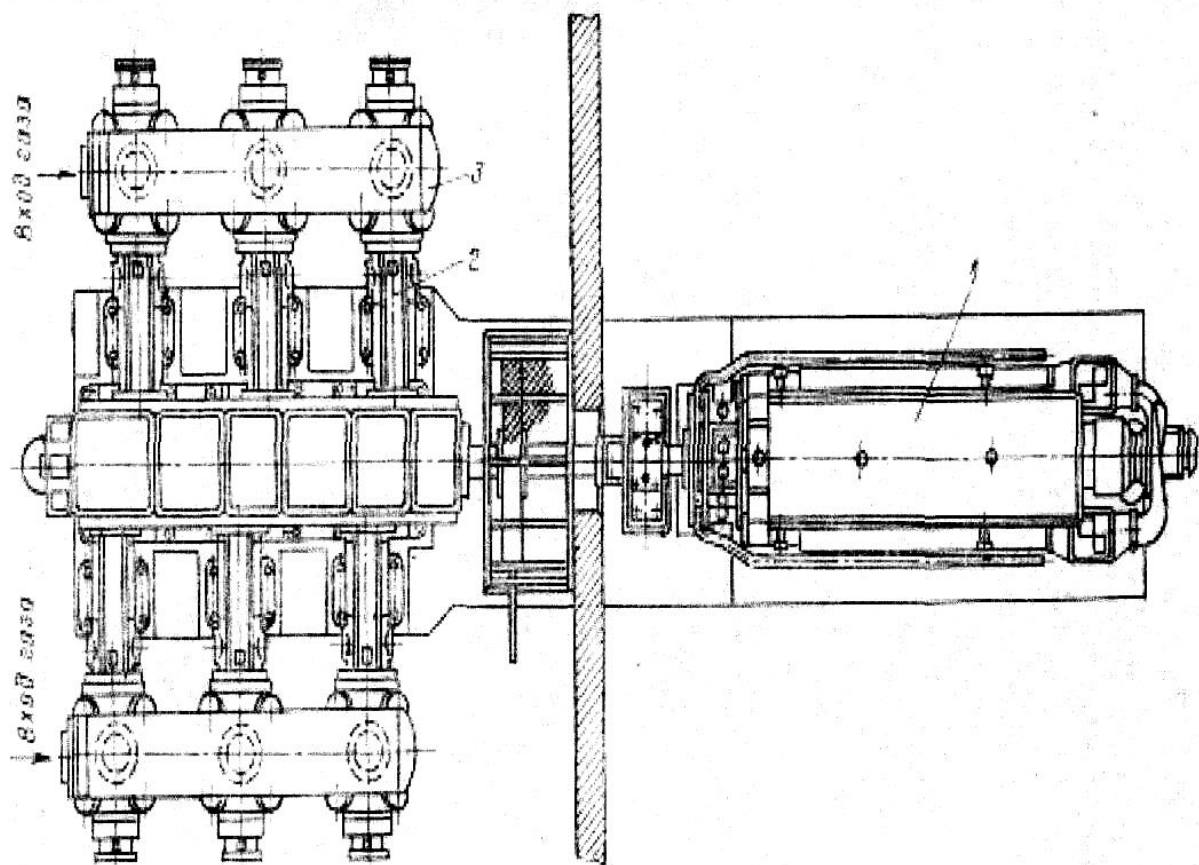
Газоперекачувальний агрегат ГПА-5000: 1 - газовий двигун; 2 - компресор;
